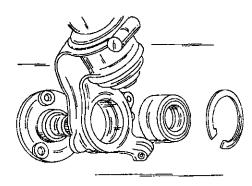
Колесный подшипник и ступица колеса, снятые с поворотного кулака. Стопорное кольцо располагается с внутренней стороны.
